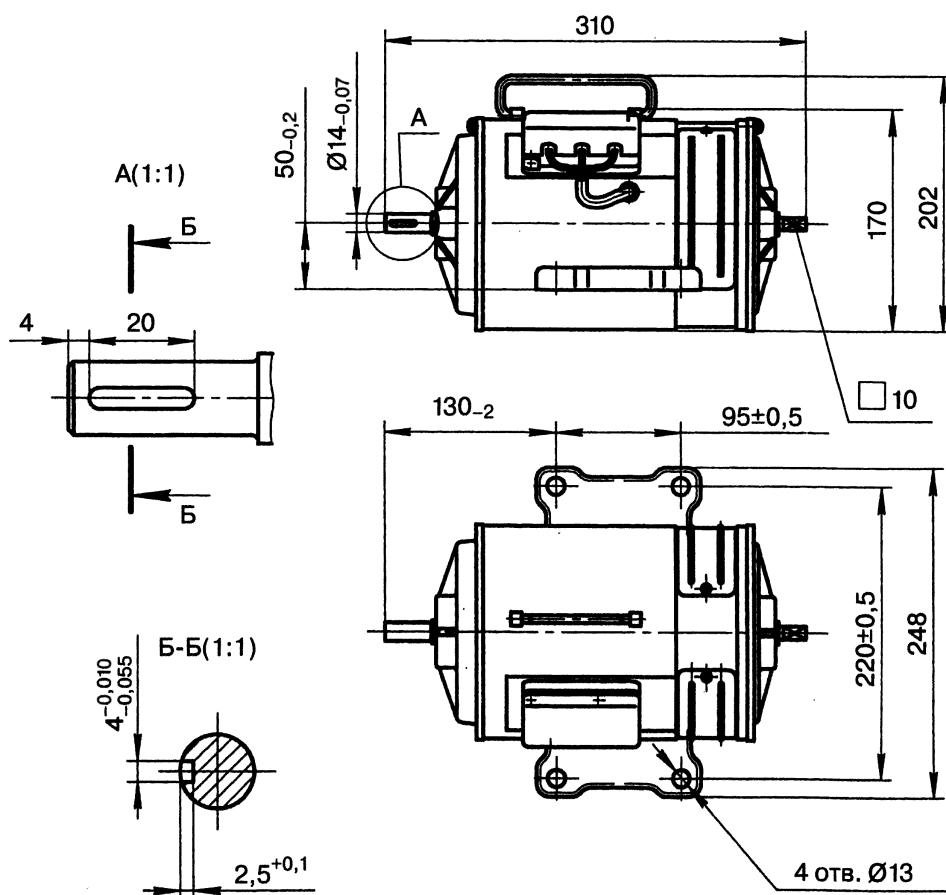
Габаритные, установочные, присоединительные размеры двигателей ДПС.
